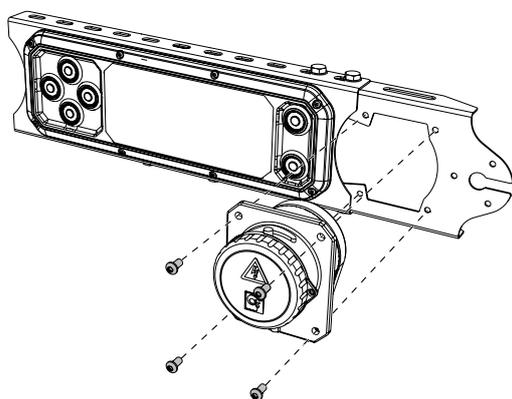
Montaje del interruptor principal junto al dispositivo de mando CD 19
